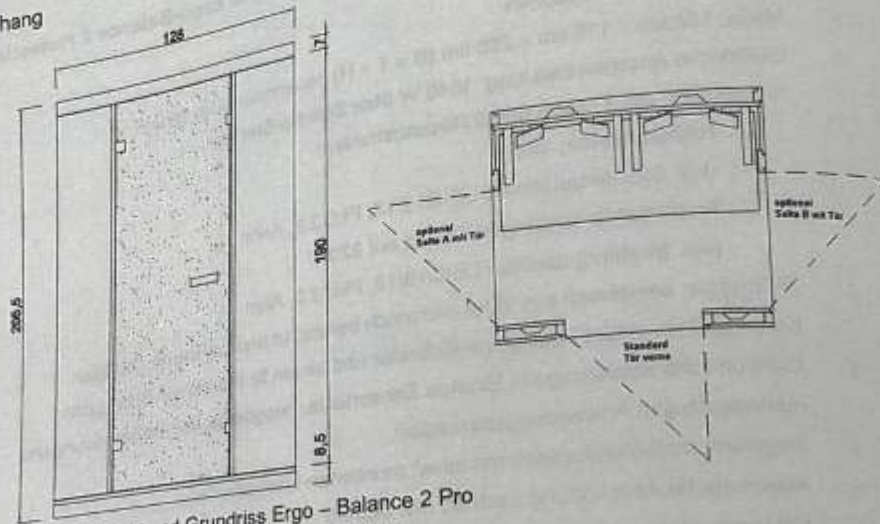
Seitenansicht und Grundriss Ergo - Balance 2 Pro
